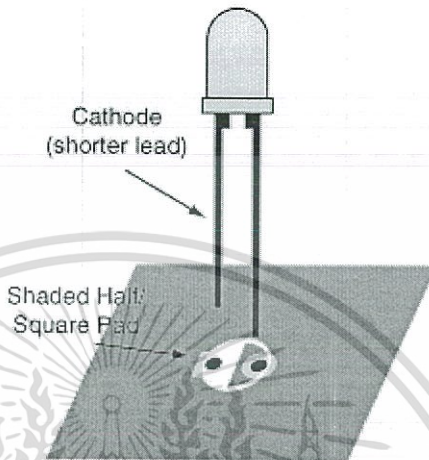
Solder Pad Diameter ที่มา [8]
